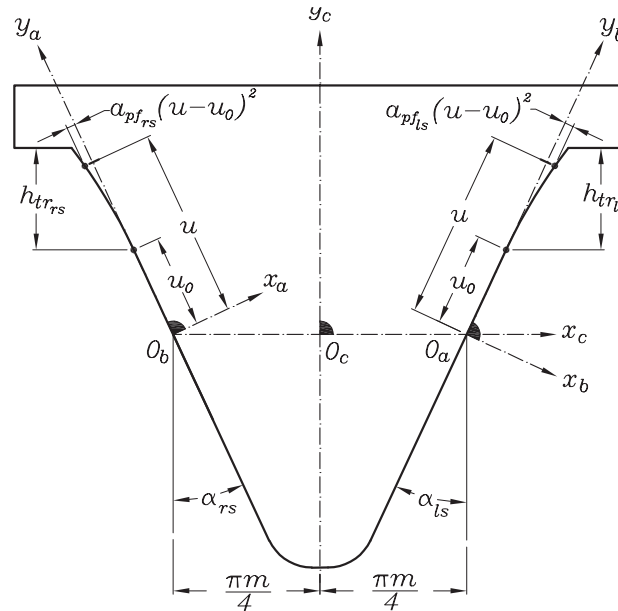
Perfil modificado de la cremallera de generación para la aplicación del rebaje de cabeza.
